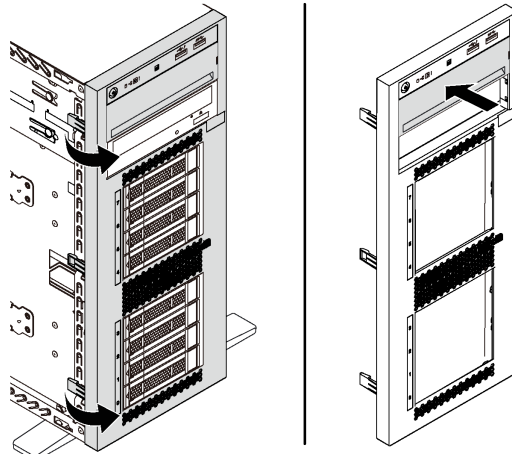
Entfernen der Abdeckung der Abdeckblende für die Laufwerkposition
